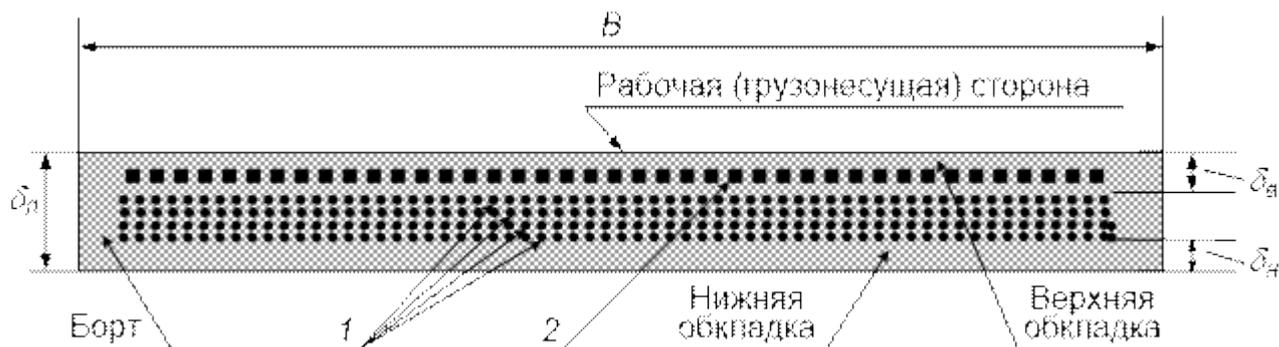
Конструкция и параметры резинотканевой ленты: B – ширина; δ_l – толщина; δ_v – толщина верхней обкладки;
